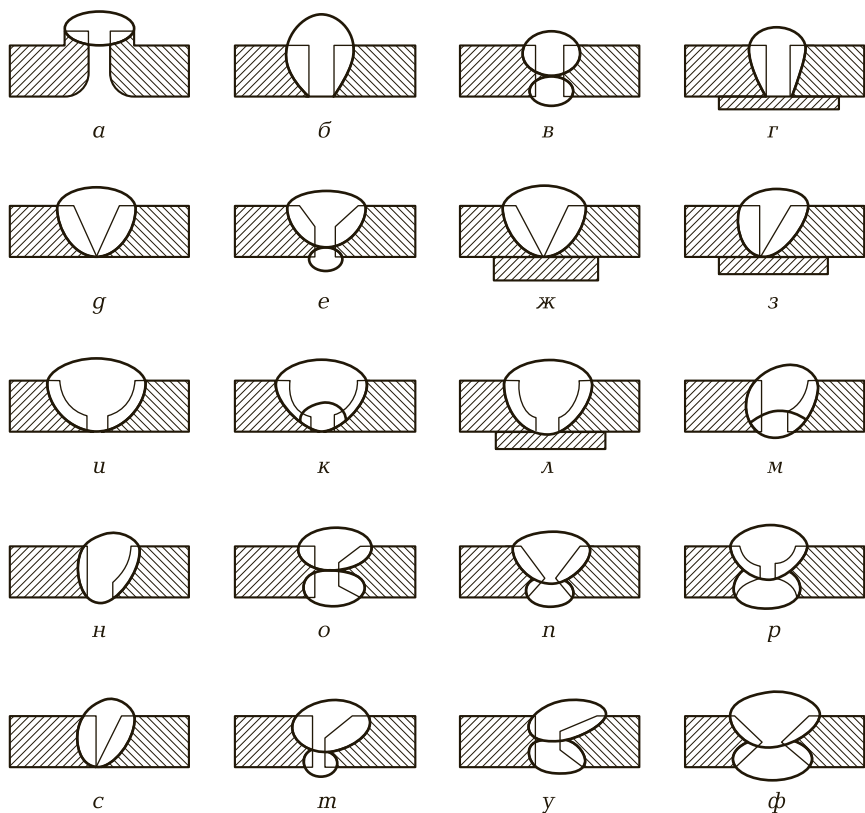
Типы стыковых сварных соединений:
